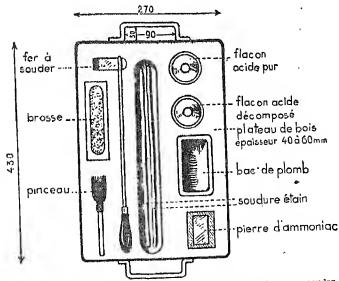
Mécessaire à souder. Tout l'outillage nécessaire pour souder est porfé par un plateau épais en hois, muni de deux anses.
